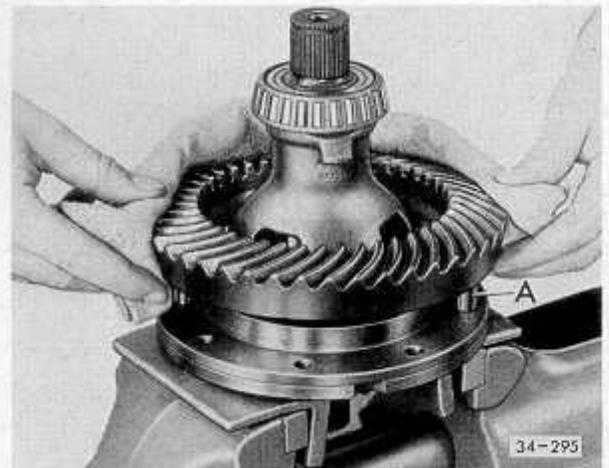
Tellerrad auf ca. 100° C erwärmen und aufsetzen.
